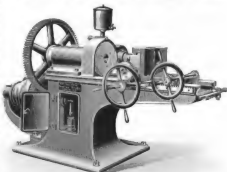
Schraubenschneidmaschine mit selbsttätiger Backenbewegung.
